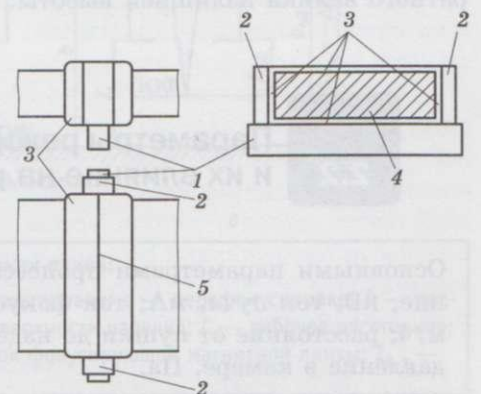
Сварные соединения типа «нахлестка через стенку»:
